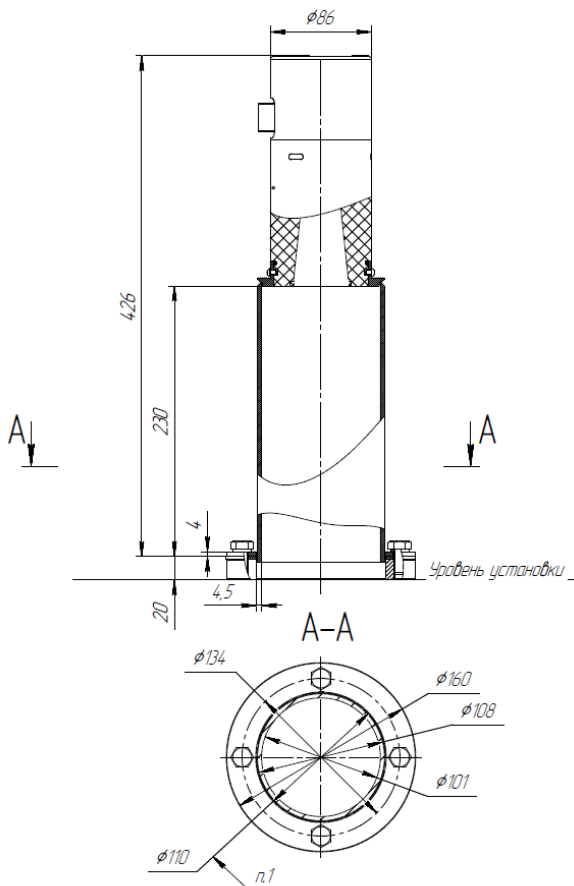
Габаритные и присоединительные размеры У-150 с герметичной стойкой
